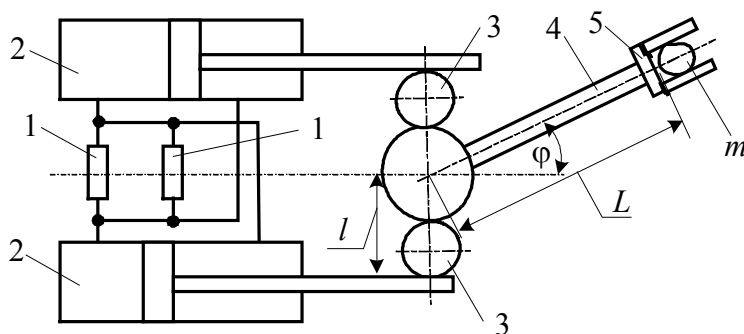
Схема поворотного привода промышленного робота «Циклон-5»: 5 — схват робота с грузом m ; 4 — рука манипулятора длиной L и массой M ; 2 — пневмоцилиндры двойного действия; 1 — распределительное устройство пневмоцилиндров; 3 — передаточный механизм с плечом l .
